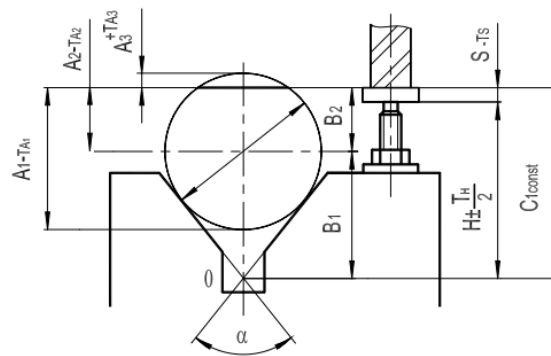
Схема установки заготовки на призму [6, с. 72]
